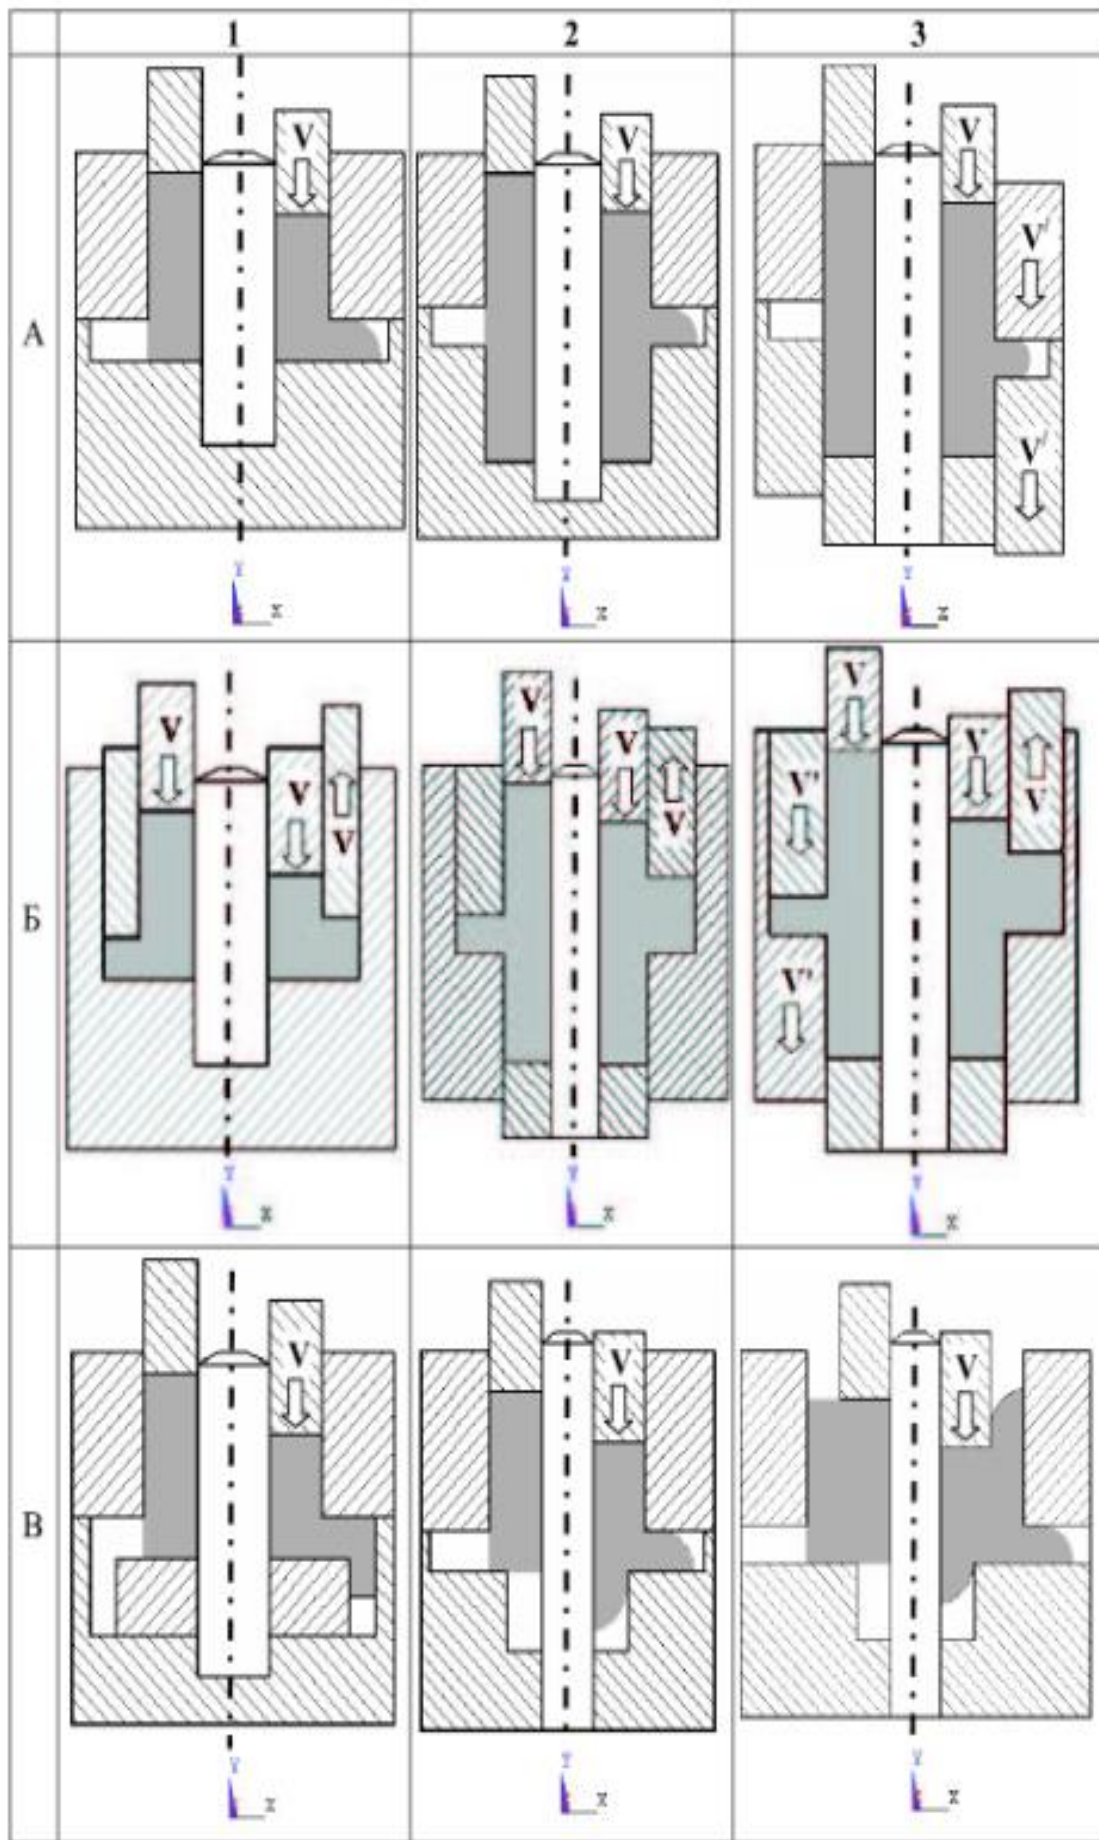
Кінематичні варіанти видавлювання із порожнистих заготовок
